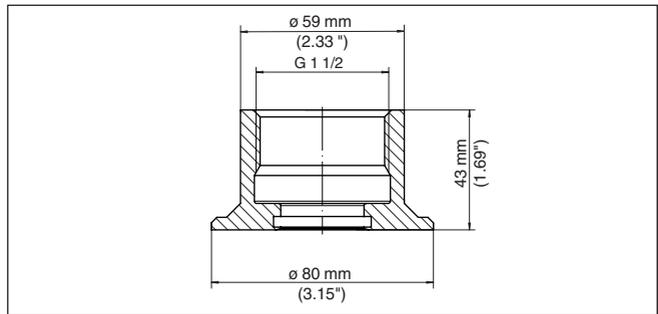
Medidas racor para soldar G1½ (DIN 3852-A)
